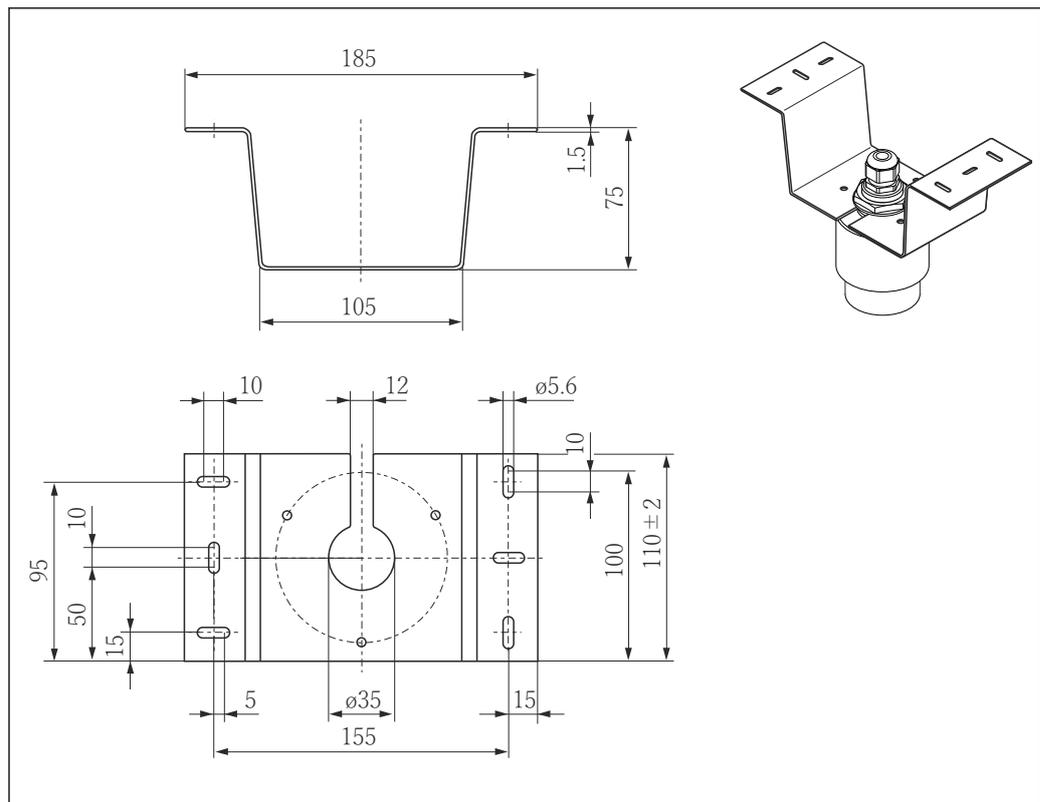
Dimensioni della staffa di montaggio per soletta. Unità di misura mm (in)
